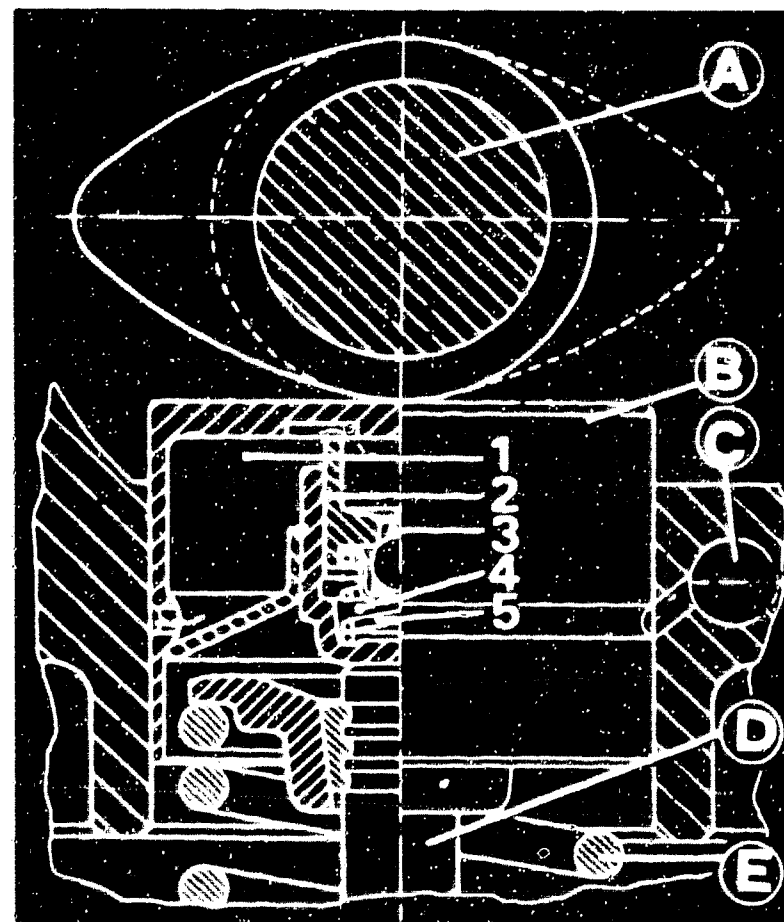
Halbschnitt durch einen hydraulischen Ventilstößel. A Nockenwelle – B Stößel mit: 1 Vorratsraum – 2 Ausfluss des Lecköls – 3 Rückschlagventil – 4 Druckraum – 5 Druckfeder – C Ölkanal – D Ventilschaft – E Ventilschaftfeder.
